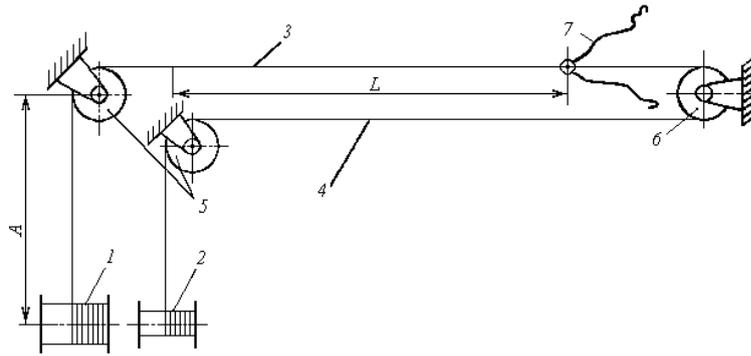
Схема работы заблокированных барабанов: 1 – грузовой барабан; 2 – барабан обратного хода; 3 – грузовой канат; 4 – канат обратного хода; 5 – блоки направляющие; 6 – блок концевой; 7 – прицепные устройства
